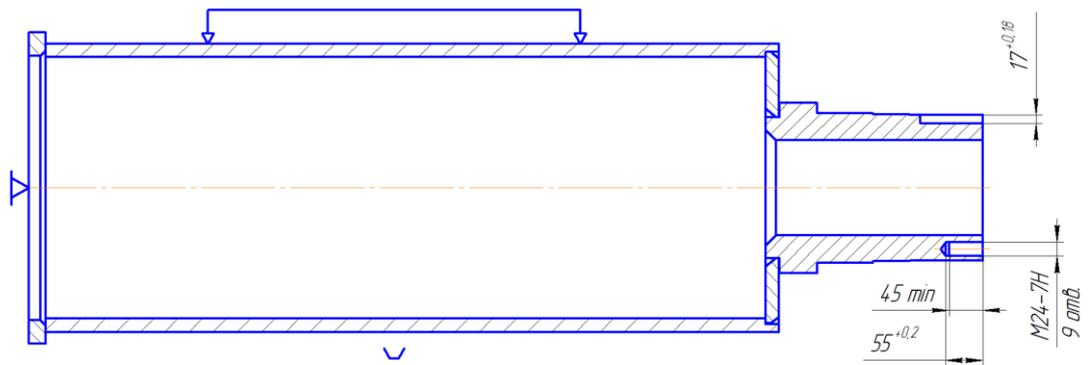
Эскиз базирования заготовки на 010 горизонтально-расточной операции.
